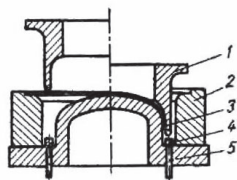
Штампування днищ за способом витяжки з перегином заготовки
